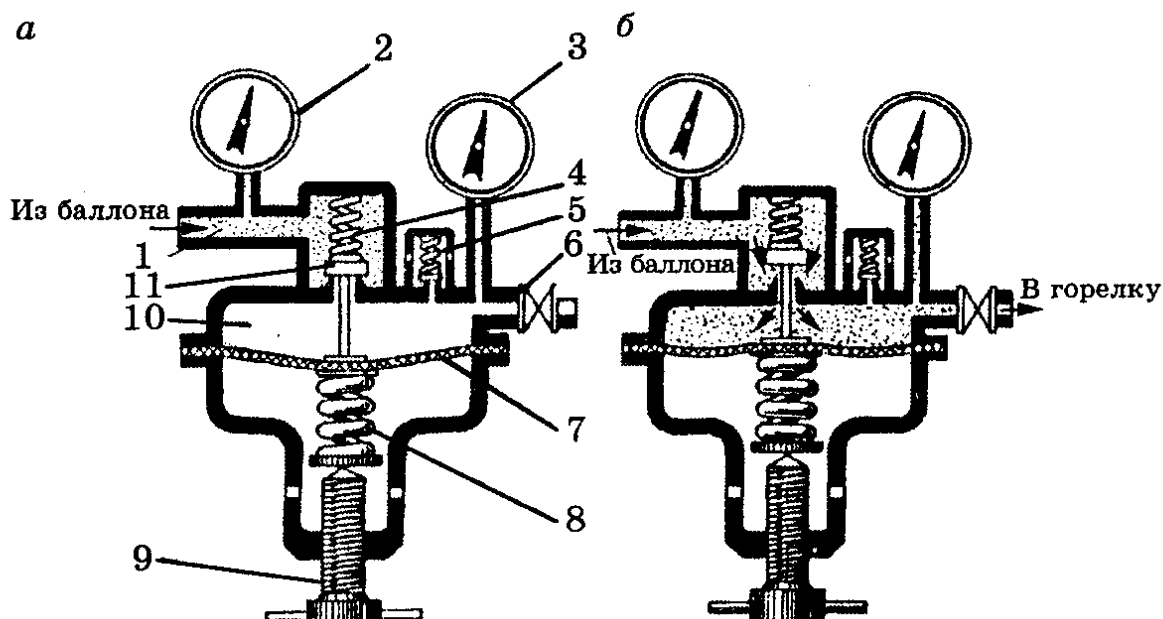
Схема устройства и работа одноступенчатого газового редуктора: а — нерабочее положение; б — рабочее положение
